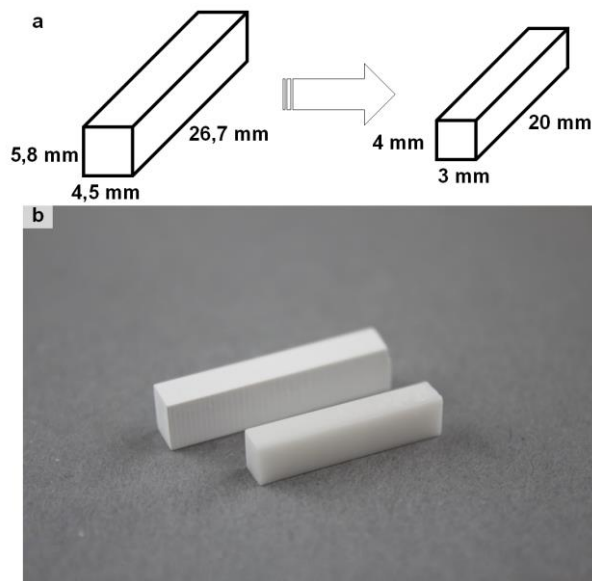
Pièces de zircon imprimées. (a) schéma des dimensions avant et après frittage et rectification, et (b) photographie d'une pièce en cru et d'une pièce frittée
